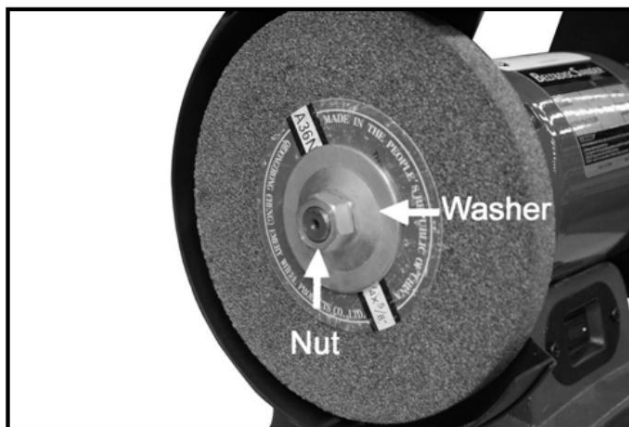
Lösen der Befestigungsmutter der Schleifscheibe
